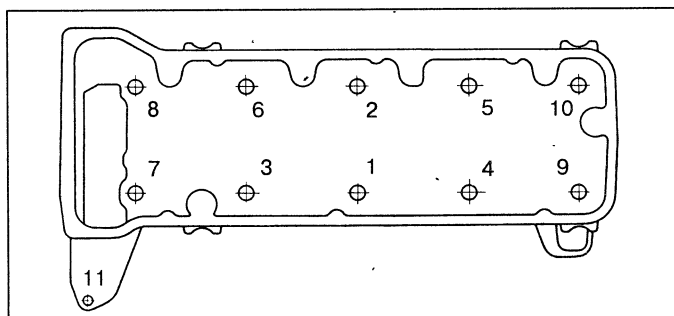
Порядок затягивания болтов головки цилиндров
